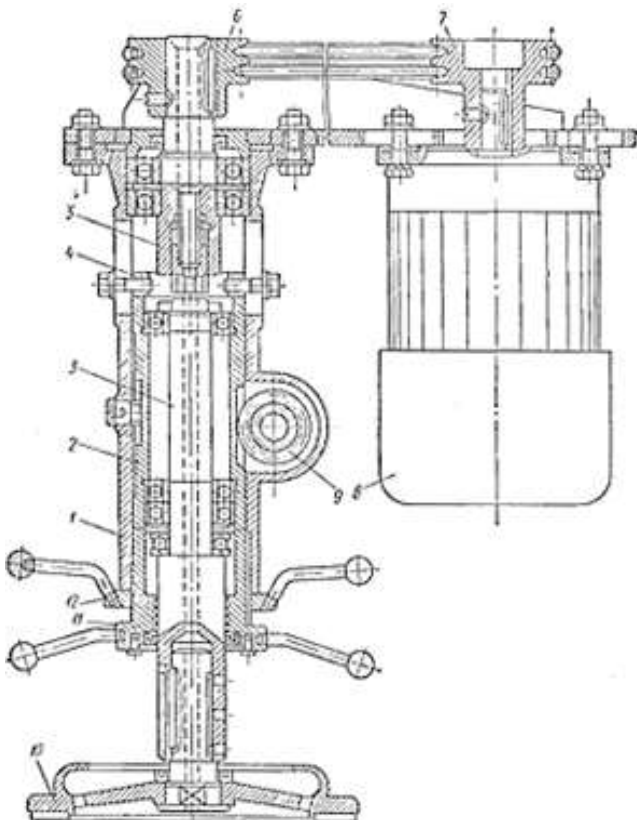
Шпиндельний вузол верстата М-011. Позначено: 1 – корпус; 2 – піноль; 3 – шпиндель; 4 – опорне напівкільце; 5 – проміжний вал; 6 – ведений шків; 7 – ведучий шків; 8 – електродвигун; 9 – рейкове колесо; 10 – корпус шліфувального круга; 11 – опорна втулка (обмежувач опускання пінолі); 12 – контргайка.
